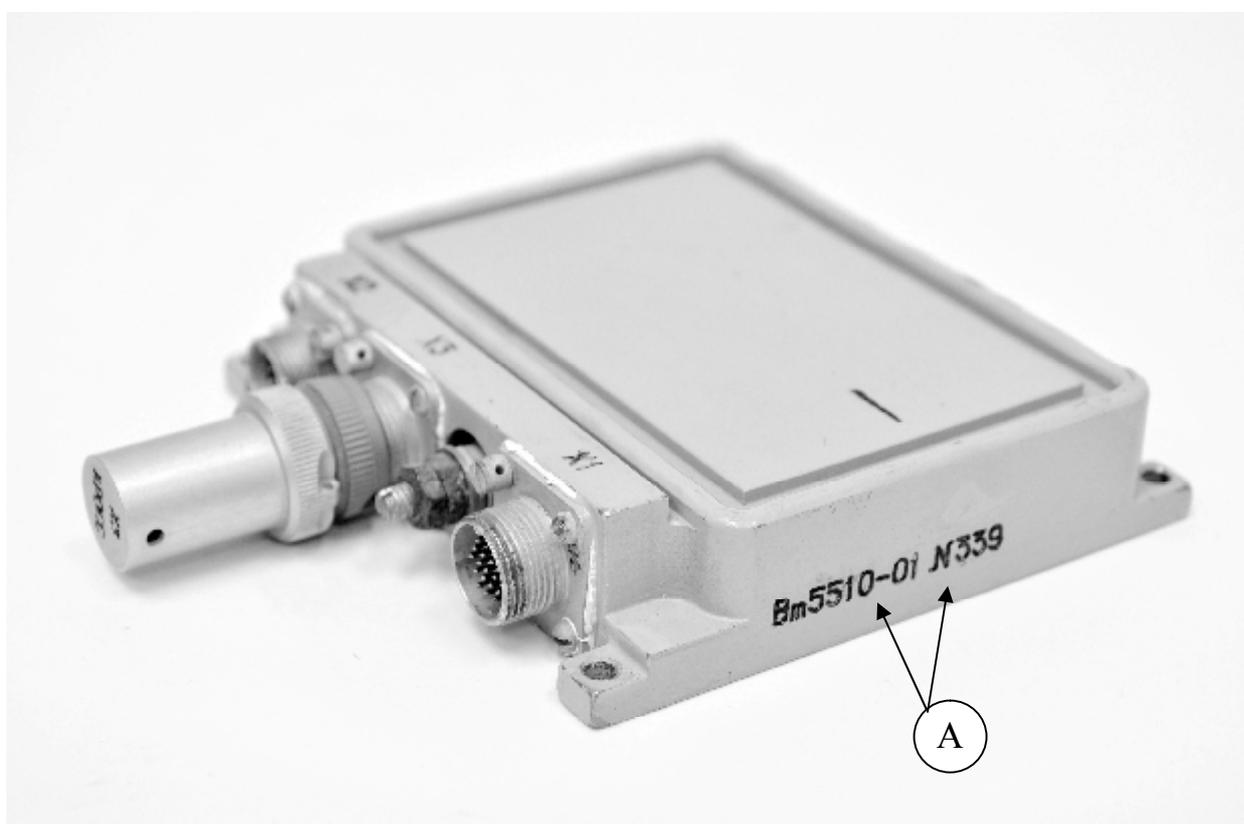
Схема обозначения мест маркировки и заводского номера
